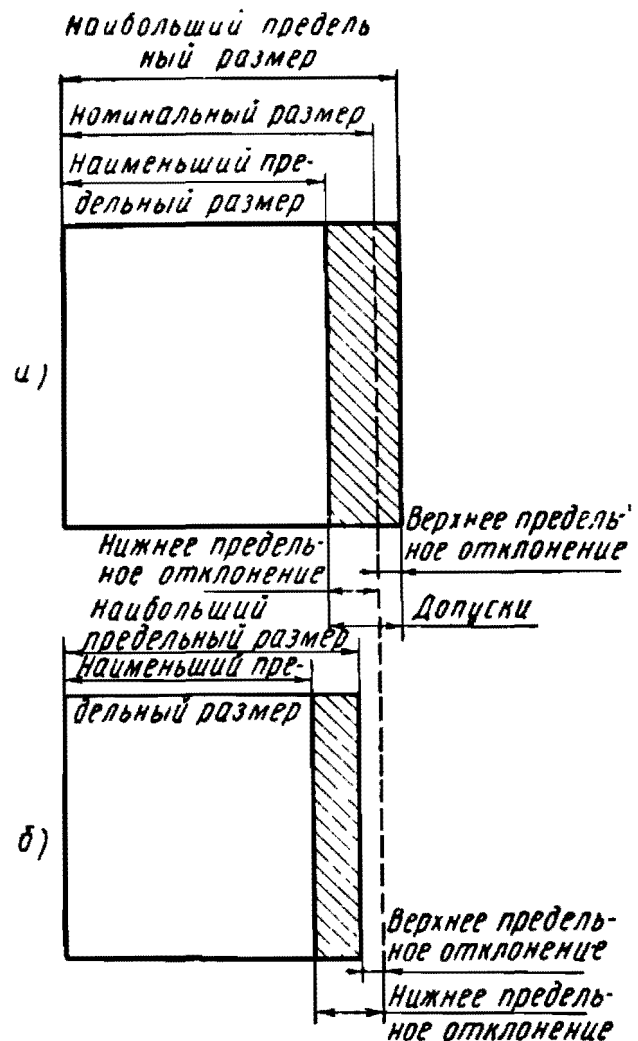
Схема расположения предельных размеров, верхних и нижних отклонений и допусков размера
